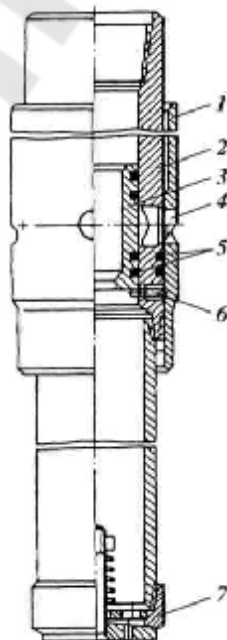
Замковый разъединитель: 1 – муфта; 2 – ниппель; 3 – запорная втулка; 4 – замок; 5 –уплотнения; 6 – срезной штифт; 7 – обратный клапан
